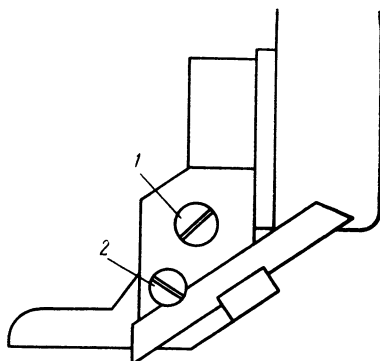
Регулировка приспособления для желобления, размещенного на лапке прессы
